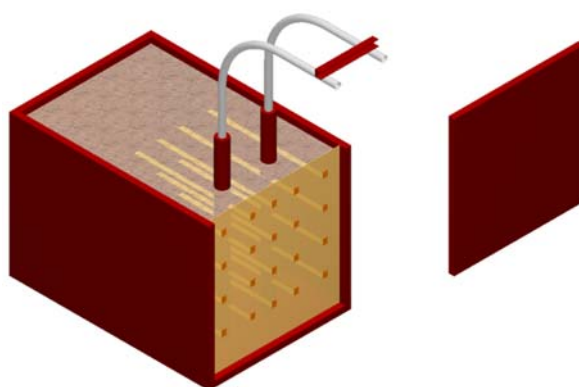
Игровая форма без съемной стенки. Выполнена ГПС, показано армирование.
